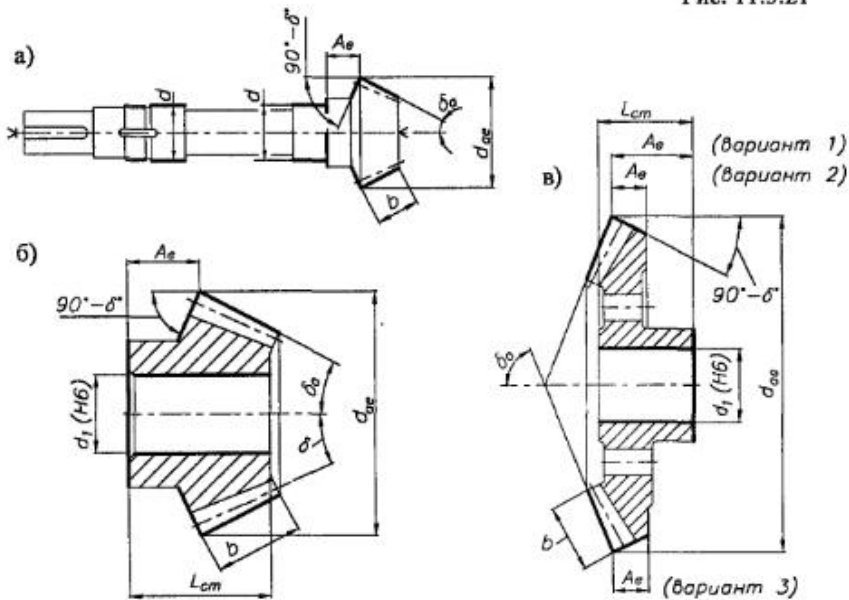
Размеры, требующие указания точности, для заготовок: а) вал-шестерни; б) шестерни; в) колеса
